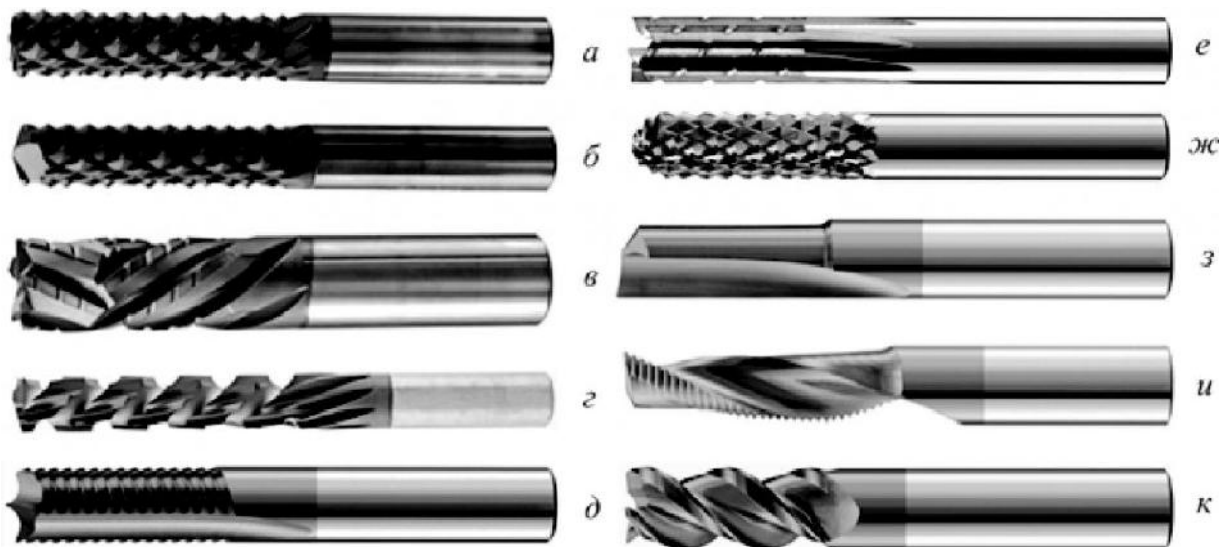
Фрезы специальной конструкции для обработки стеклопластика. а – борфреза с перекрестной насечкой; б – борфреза с перекрестной насечкой и сверлом; в – фреза с разнонаправленными спиральными канавками; г – многозубая фреза с большим углом наклона стружечных канавок; д – борфреза с обратным режущим торцом; концевая фреза с прямым зубом и стружко-разделительными канавками; ж – сферическая концевая фреза с перекрестной насечкой (конструкция «кукуруза»); з – концевая фреза $z=1$, прямой зуб для высокоскоростной чистовой обработки; и – однозубая концевая фреза для высокоскоростной обработки, $z=1$, правая спираль, прерывистая режущая кромка; к – концевая фреза, $z=3$, спираль 45° , с неравномерным шагом режущих кромок.
